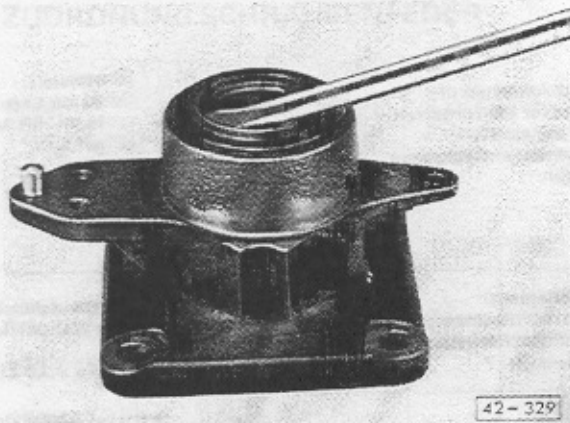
Dichtringe mit Montierhebel ausdrücken
